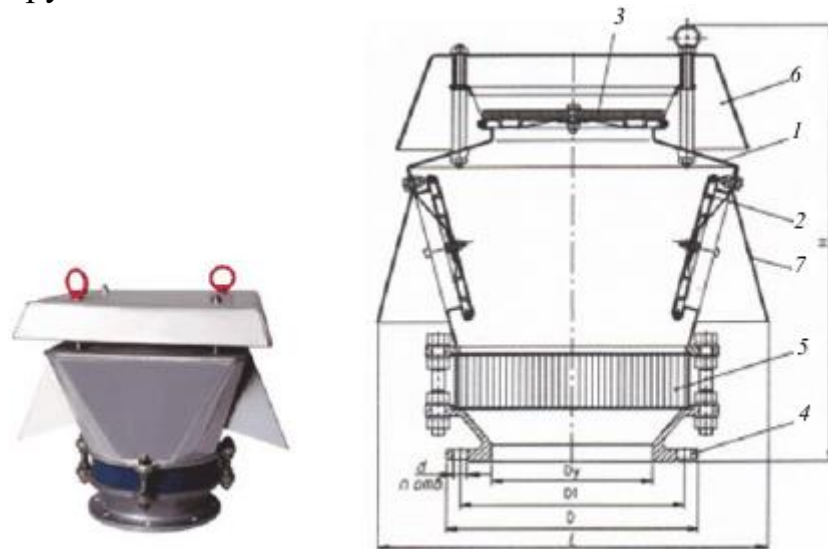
Клапан КДМ-200: 1 - корпус; 2 - тарілка вакууму; 3 - клапан тиску; 4 - приєднувальний фланець; 5 - вогневий запобіжник; 6 - кришка; 7 – козирок
